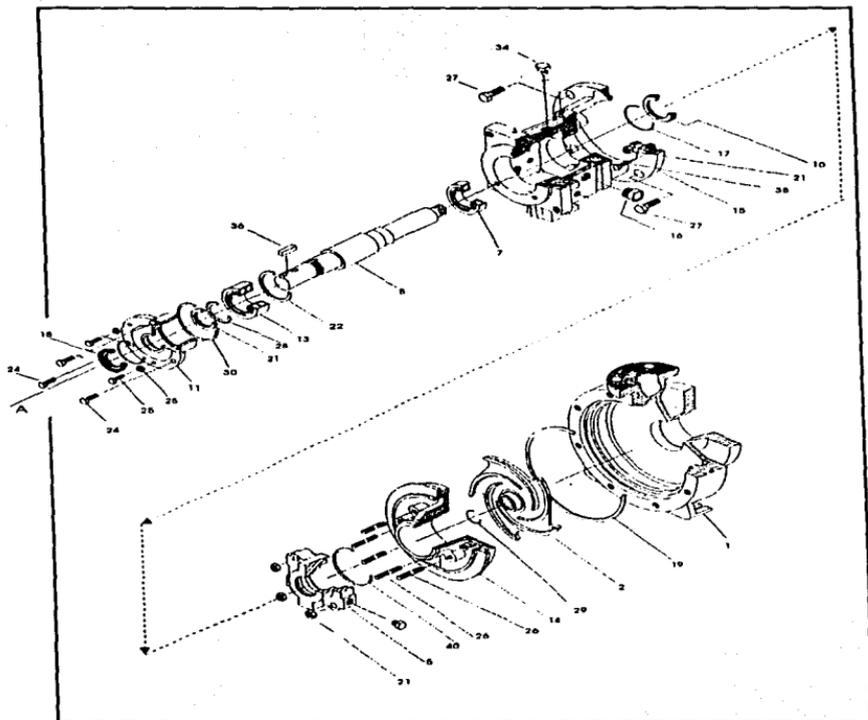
Dibujo explosivo de la Bomba Centrífuga
